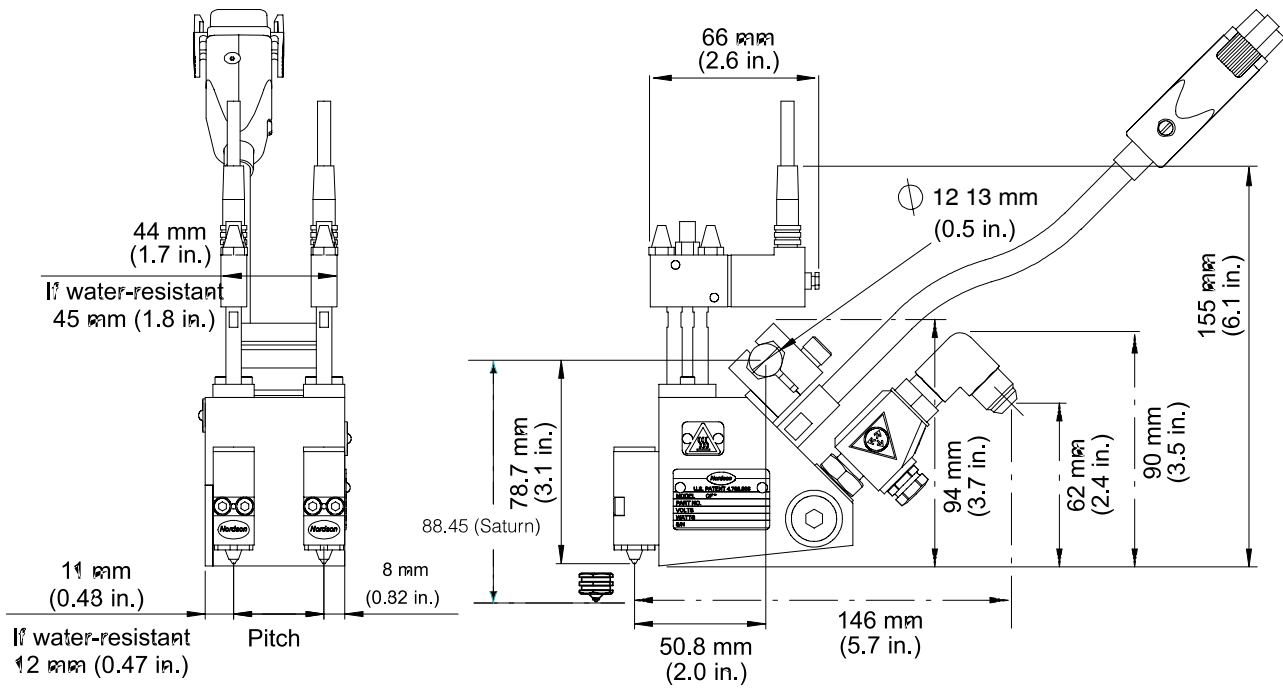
Dimensiones de una pistola configurable de varios módulos con una electroválvula SD
